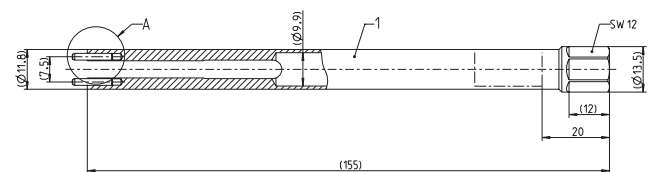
Montageschlüssel ø11,8/SW12 Typ 1300A73 für Einbaubohrung ø12 mm
